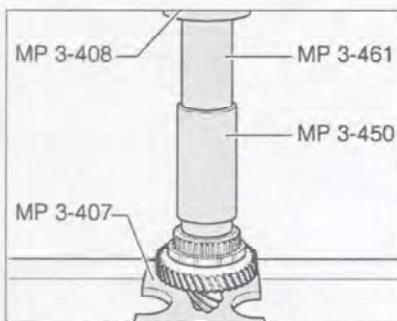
Установка ступицы синхронизатора 1-й/2-й передач.
